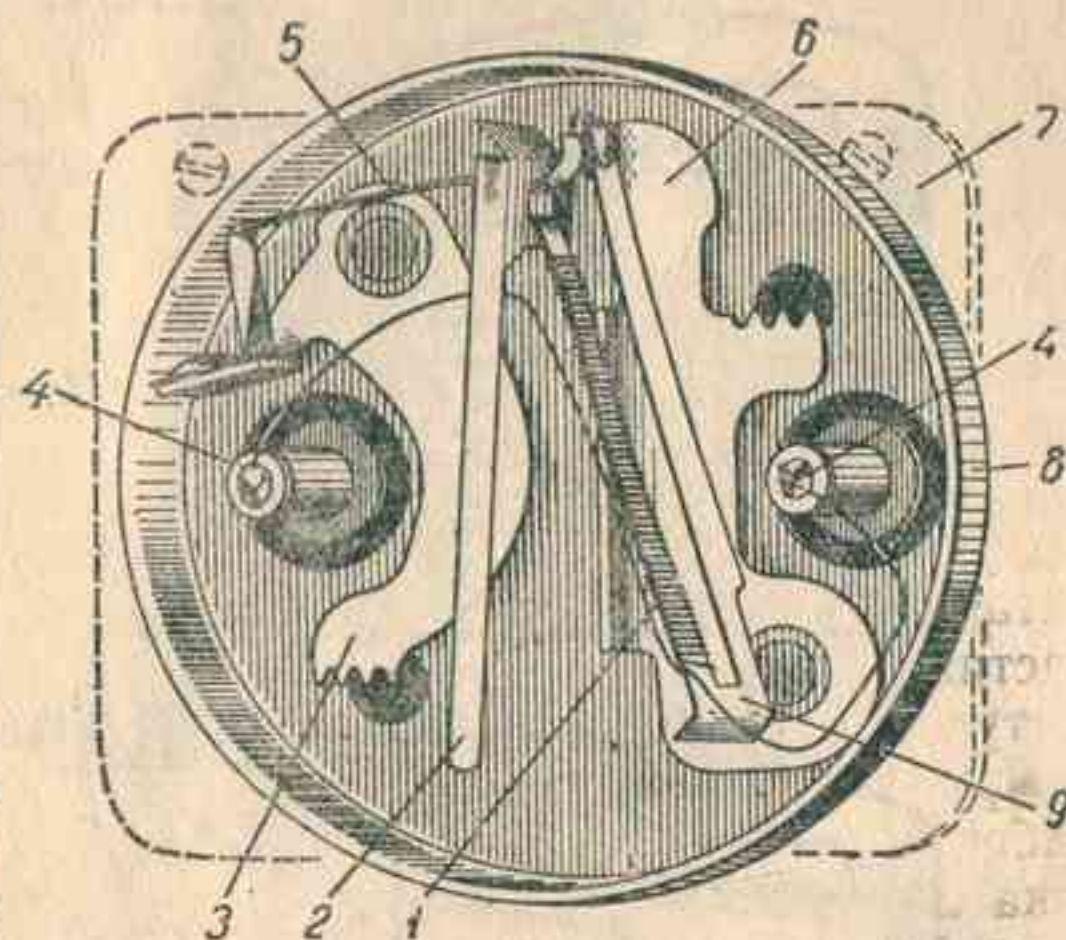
Приемник термометра (без шкалы): 1 — обмотка; 2 — стрелка; 3, 6 — зубчатые секторы (для регулировки); 4 — клеммы; 5 — упругая пластина (пружина стрелки); 7 — основание; 8 — корпус; 9 — биметаллическая пластина
